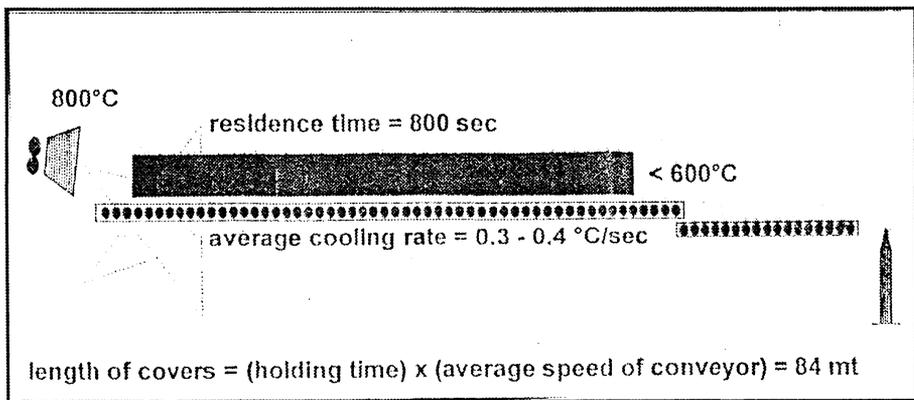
Металлургические принципы медленного охлаждения сварочной катанки на роликовом конвейере «Стелмор»
